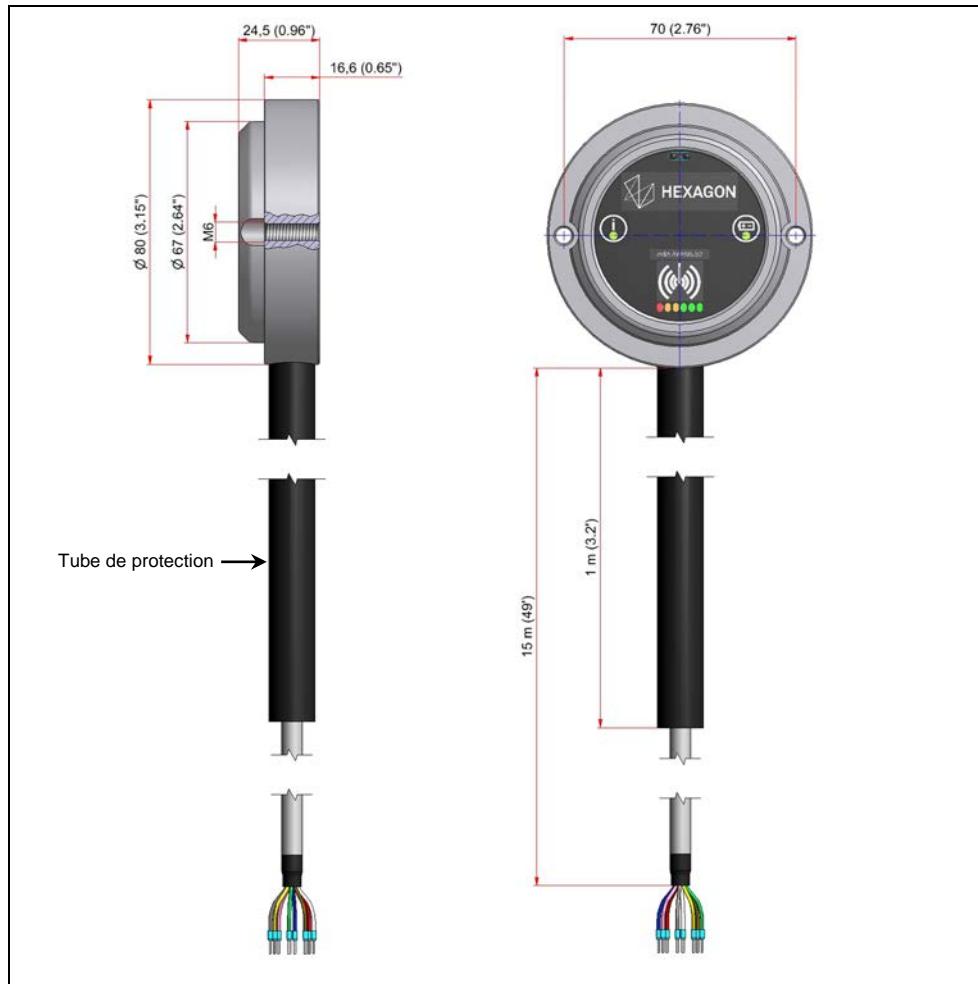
Dimensions RWR95.50-R (sortie radiale de câble)
